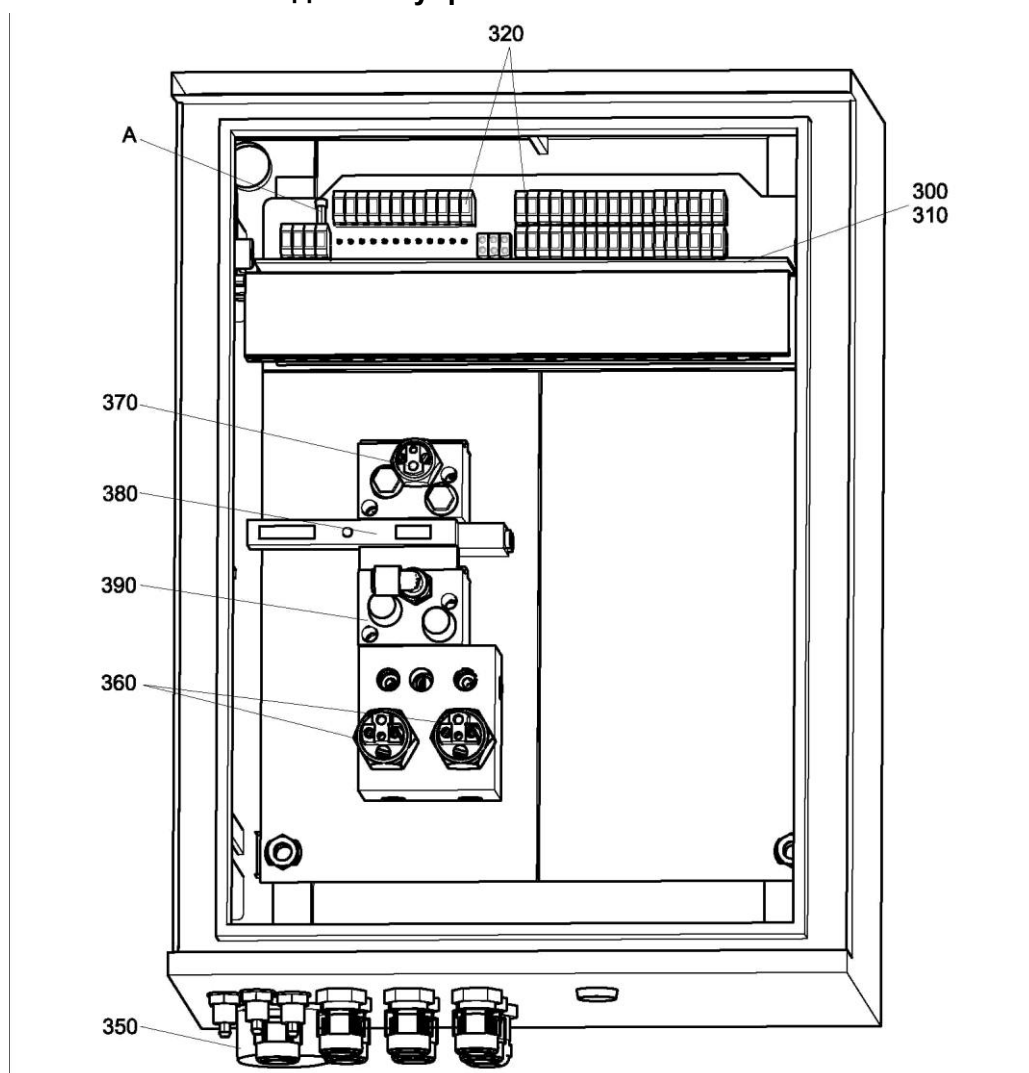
Общий вид корпуса CPG30 A Предохранитель
